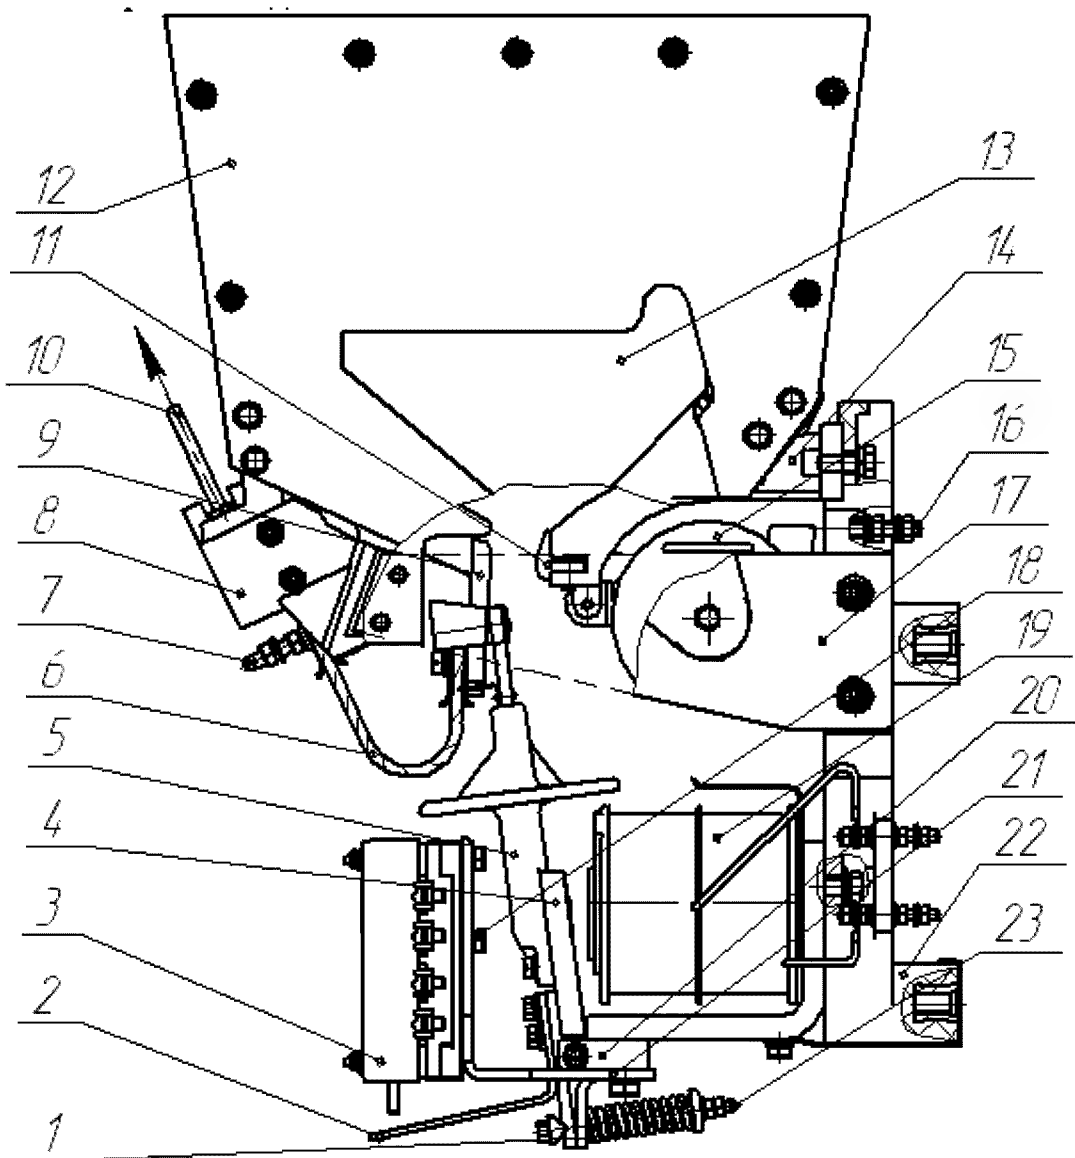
Конструкция и габаритные размеры контактора 1KM.016M
